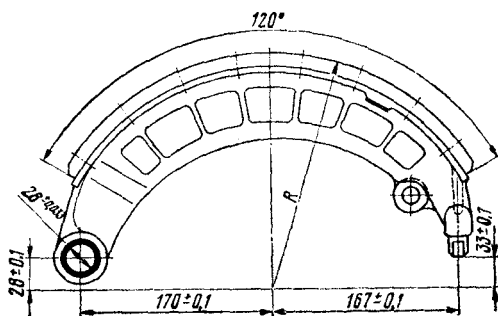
Размеры для установки колодки рабочего тормоза при механической обработке накладок
